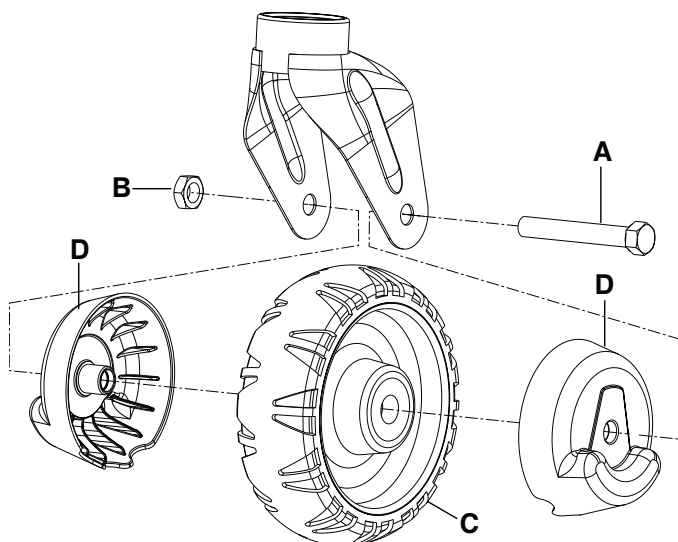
Колеса каталки с колесными колпаками без стопора колес
